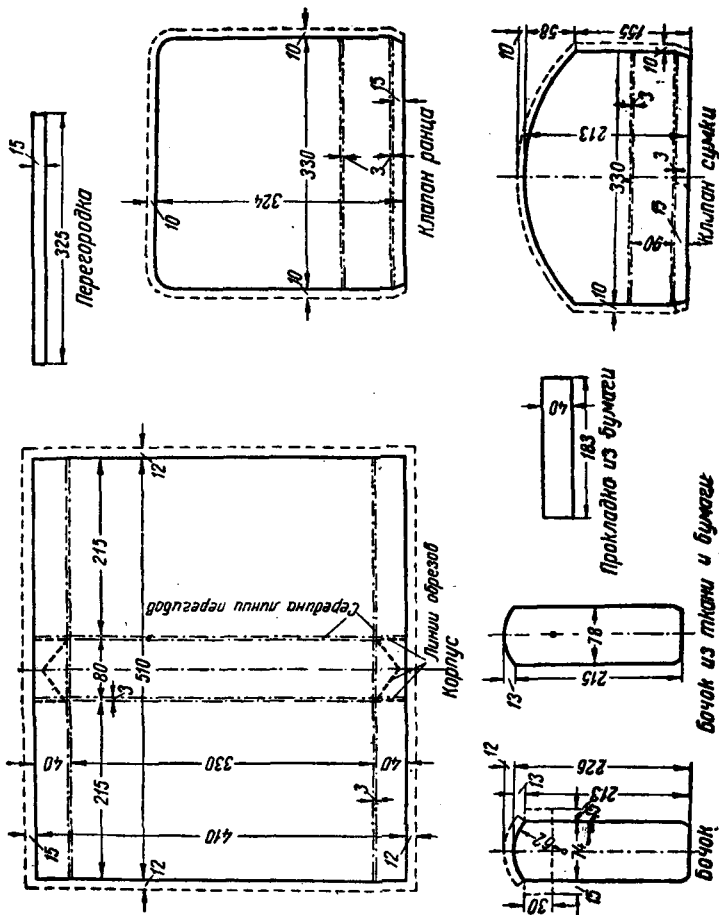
Чертеж деталей сумки размером 25 × 18 × 7 см
